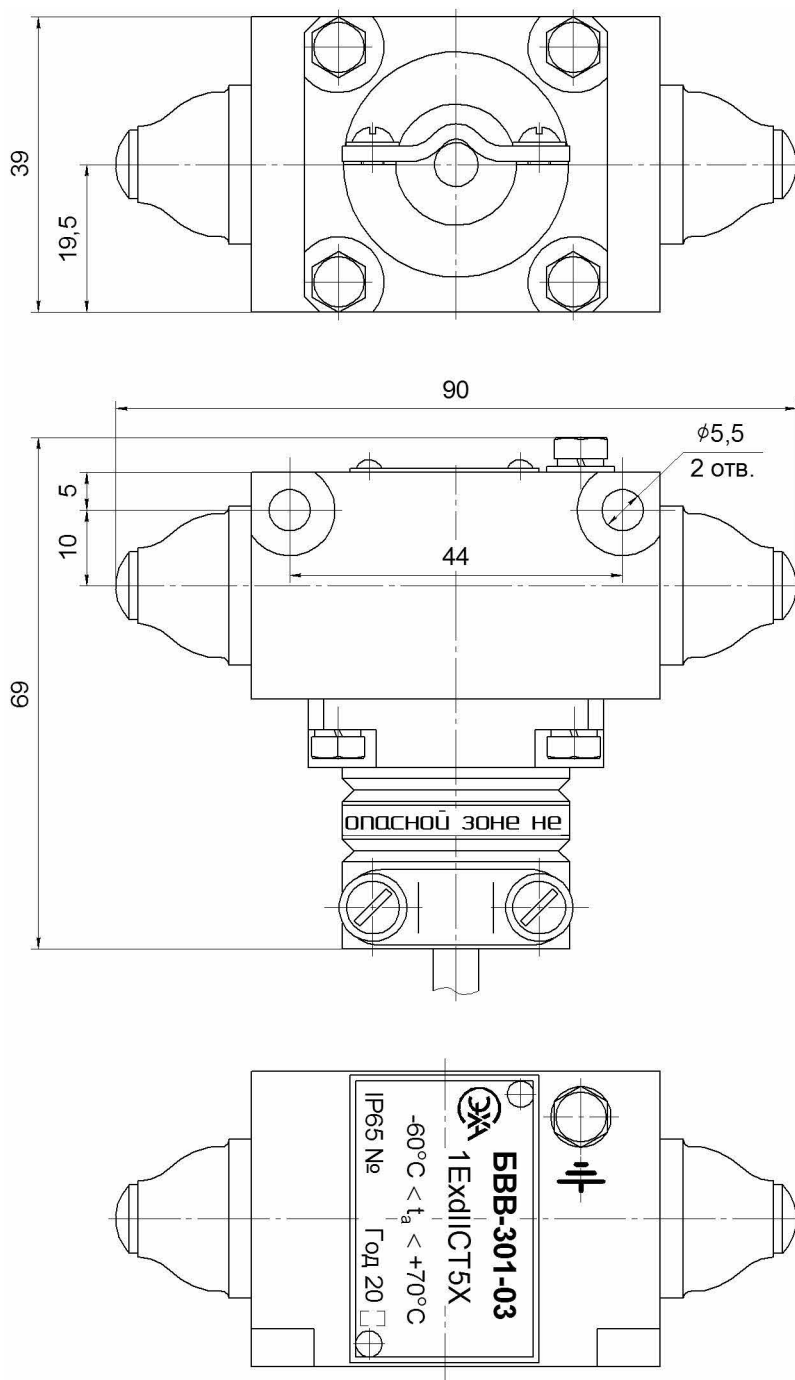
Габаритные и установочные размеры блока выключателей БВВ-301-03
